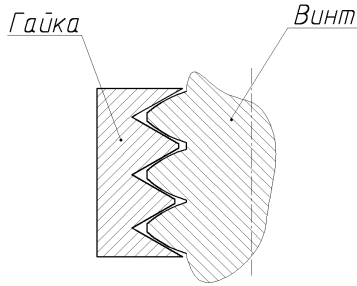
Резьбовое сопряжение гайки с треугольным профилем резьбы и винта с выпуклым профилем резьбы
